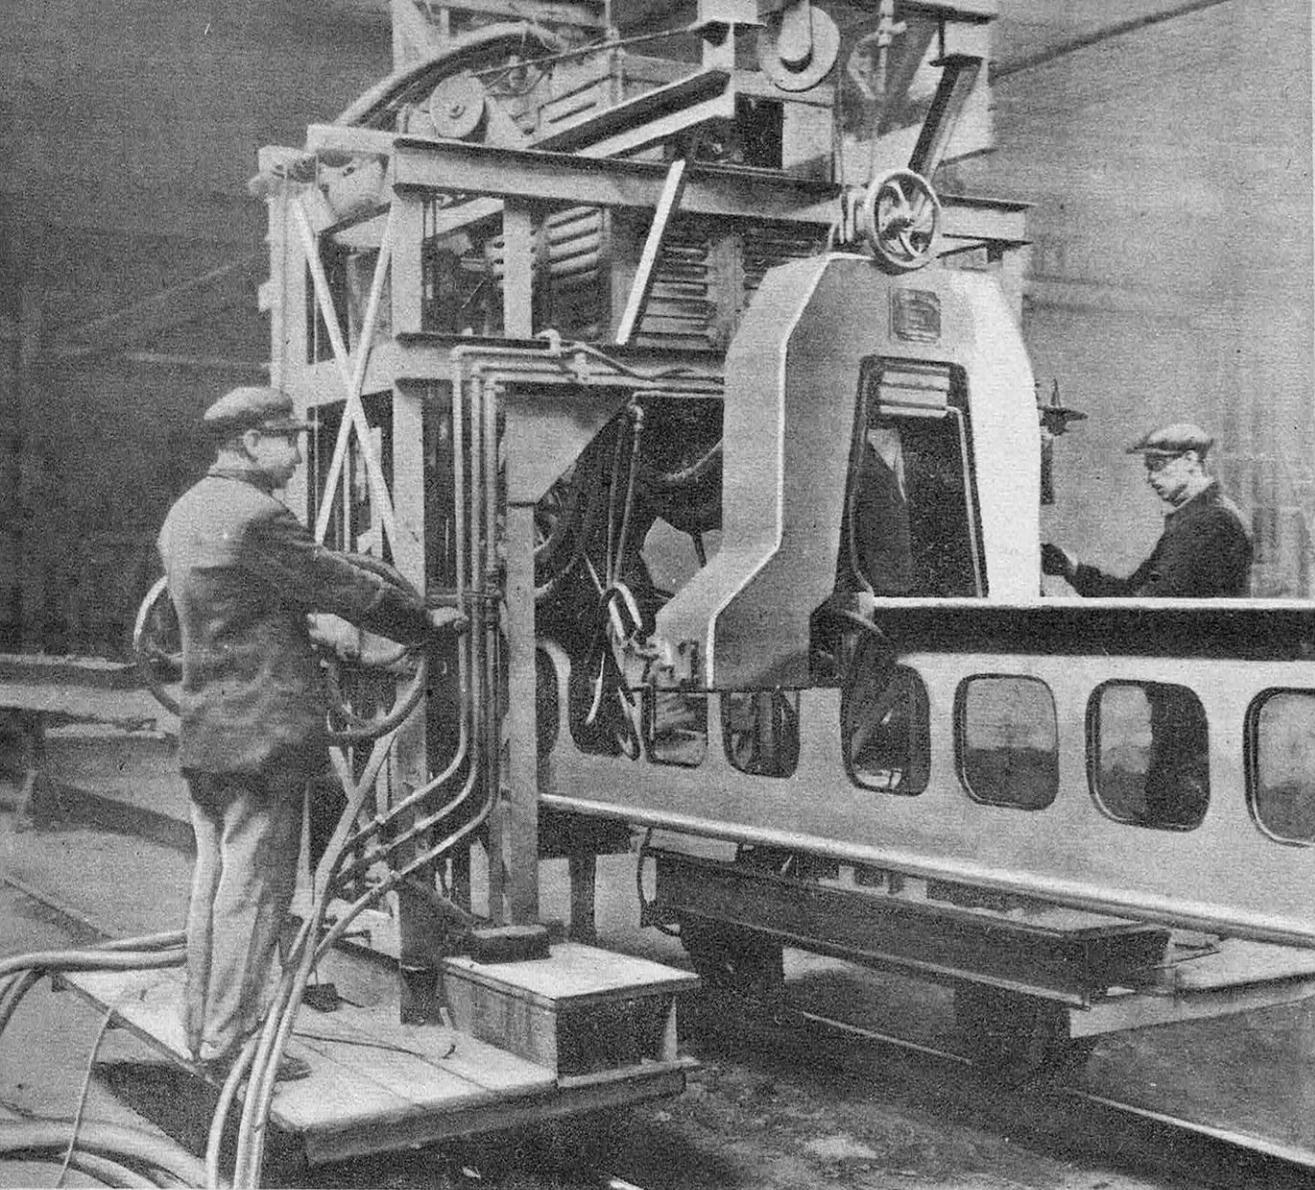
PINCE A SOUDER PAR POINTS MONTÉE SUR RAILS
